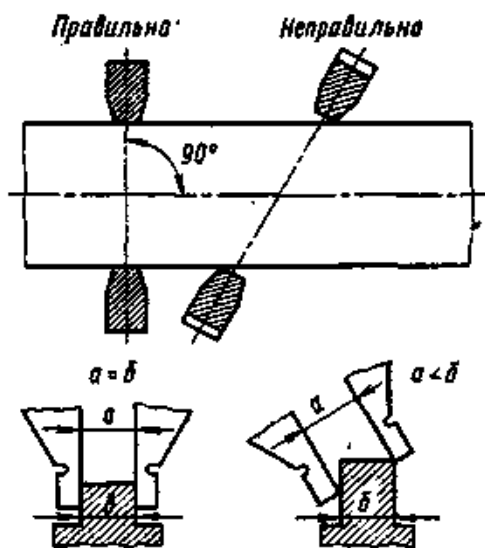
Установка штангенциркуля при измерении наружных поверхностей
